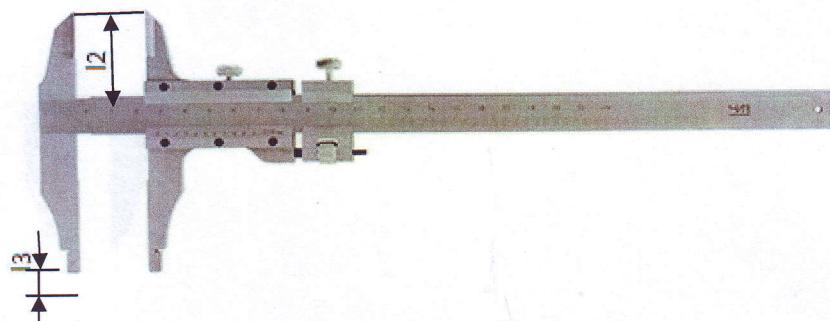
Штангенциркуль ШЦ-ІІ
